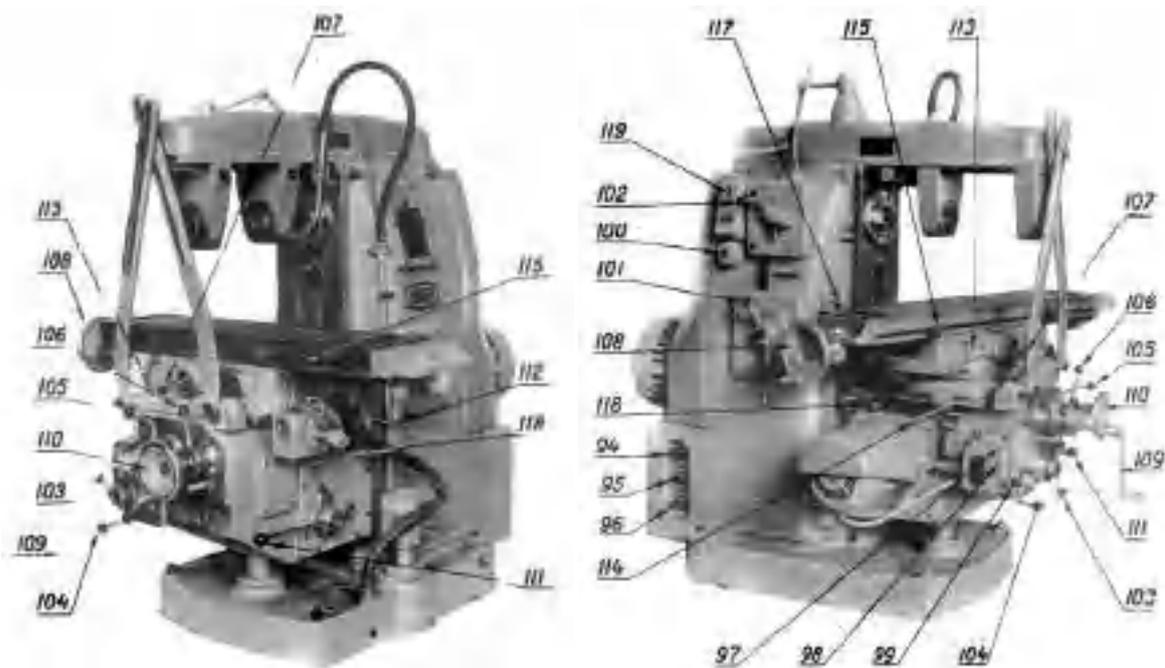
Расположение органов управления фрезерным станком модели 6Н81Г
